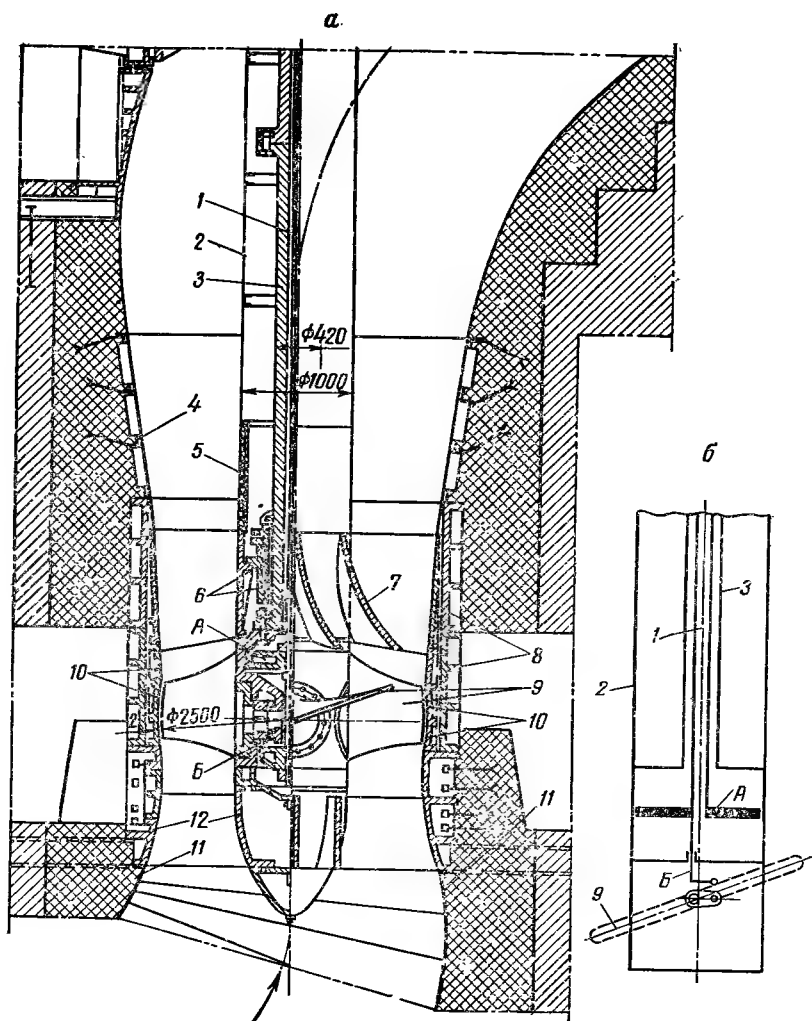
Конструкция рабочей части (*a*) и схема механизма поворота лопастей (*б*) насоса ВП-250:
